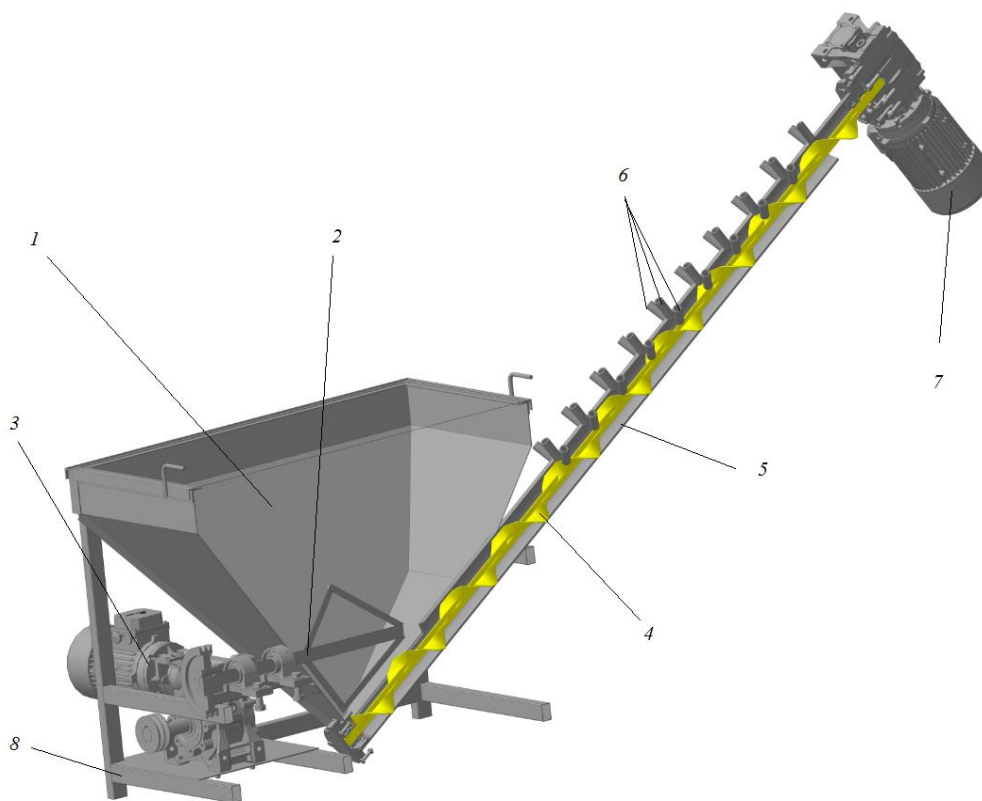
3D-модель механізму перемішування сировини для виготовлення брикетів розпалювання (переріз)
